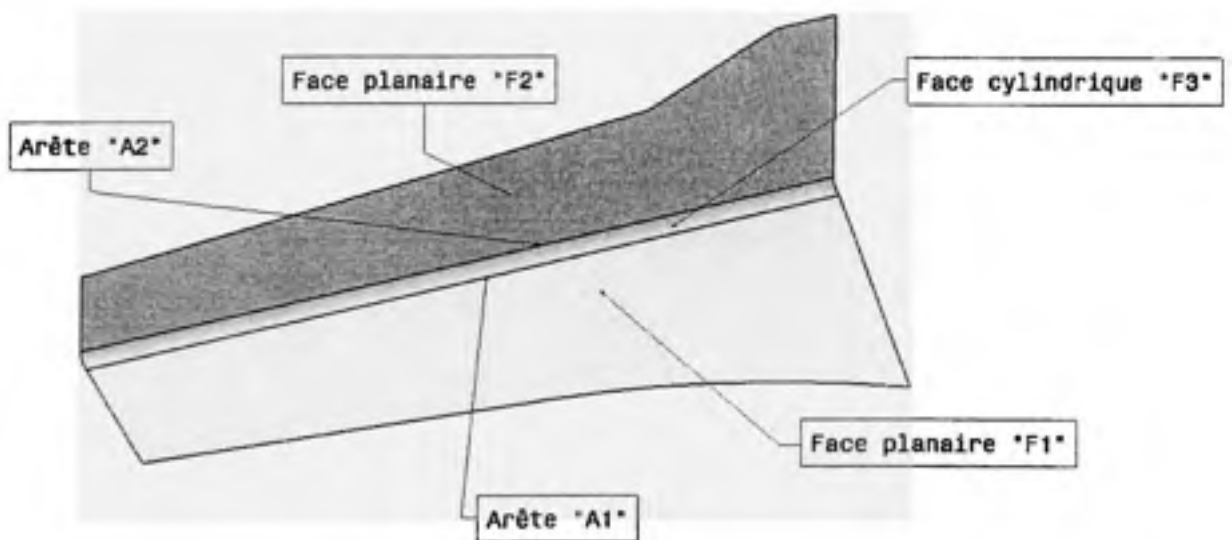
FAAG - Définition des surfaces et des arêtes d'un flanc
